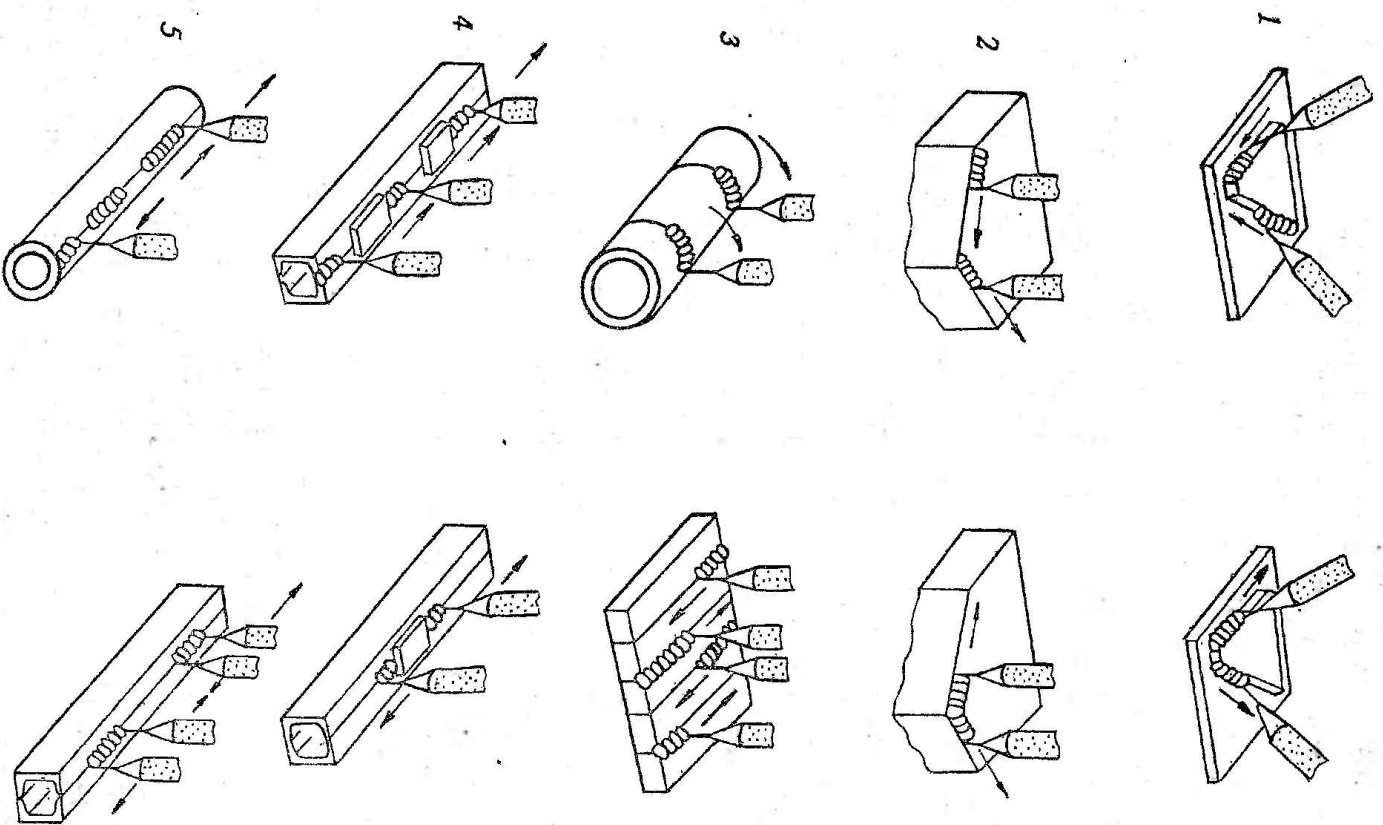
Виды сварки многоугловыми автоматами
